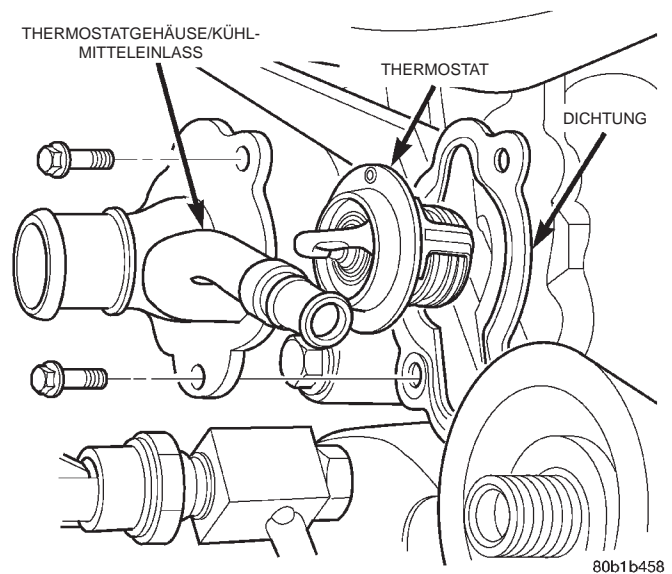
Thermostat und Thermostatgehäuse—3.2L-Motor
